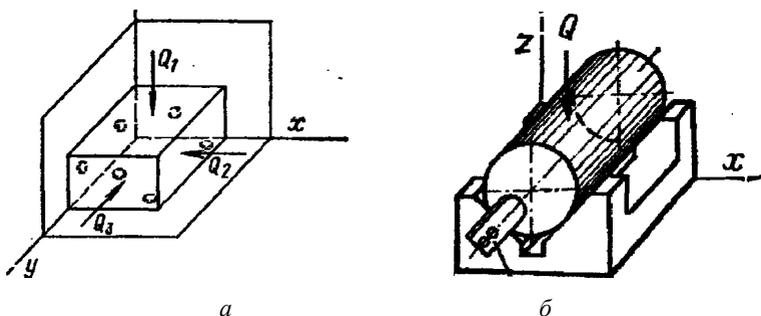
Схема закрепления (направления прижатия) деталей:
